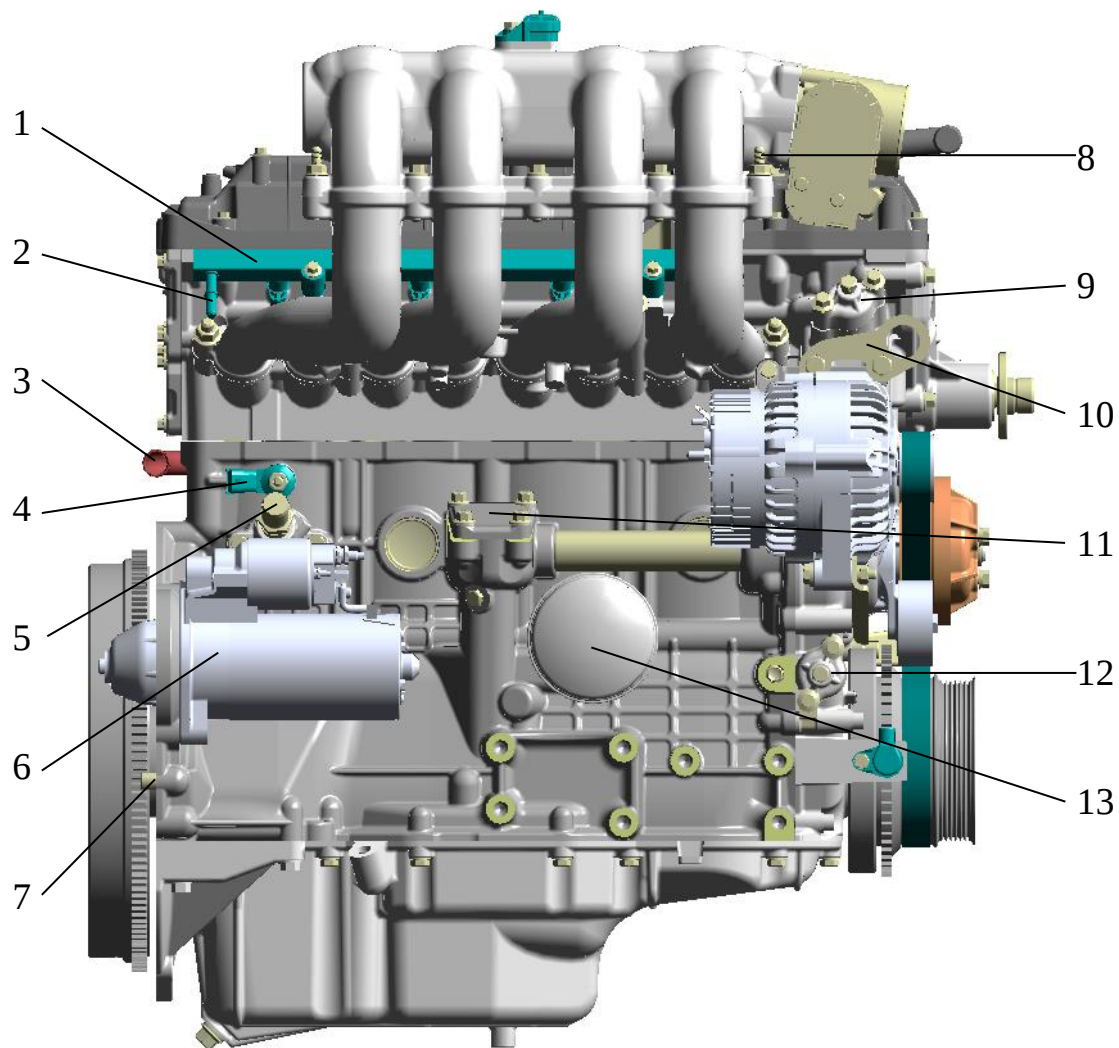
Вид двигателя 3МЗ-409051.10 слева:
